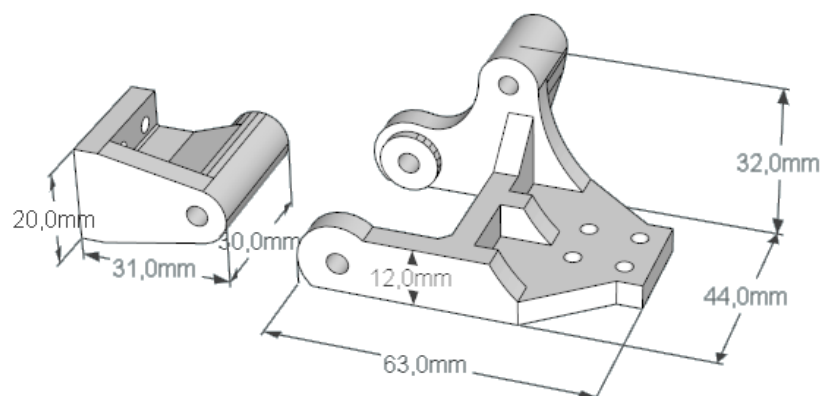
Модель деталей шарнирного соединения манипулятора в области схвата
